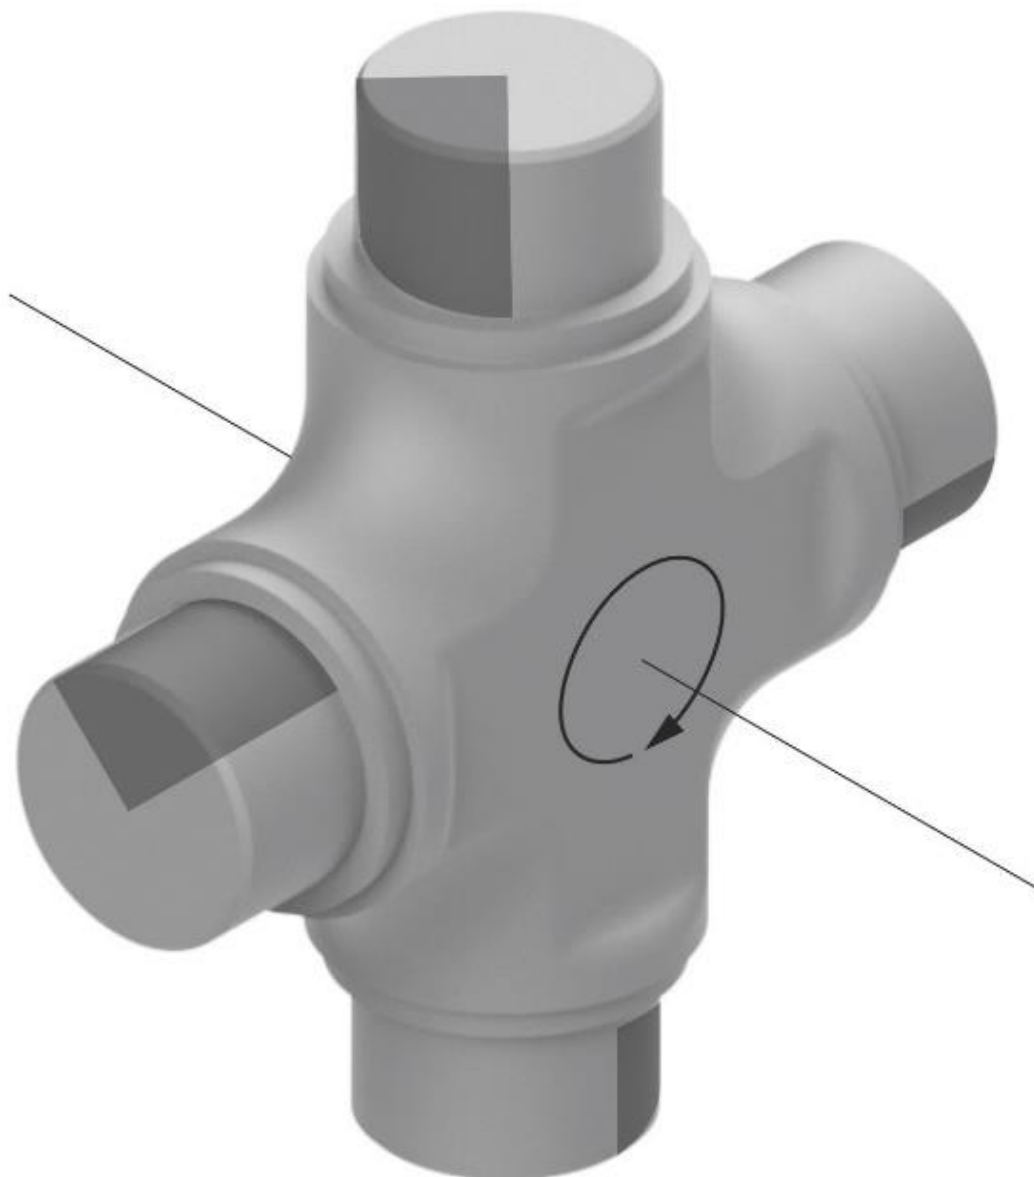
Схема расположения зон контакта шипов крестовины
